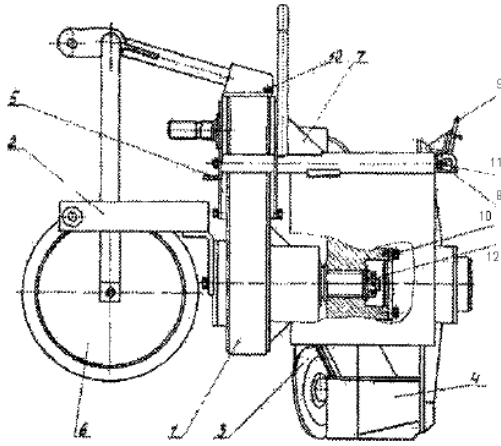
Агрегат лесопожарный фрезерный АЛФ-10
